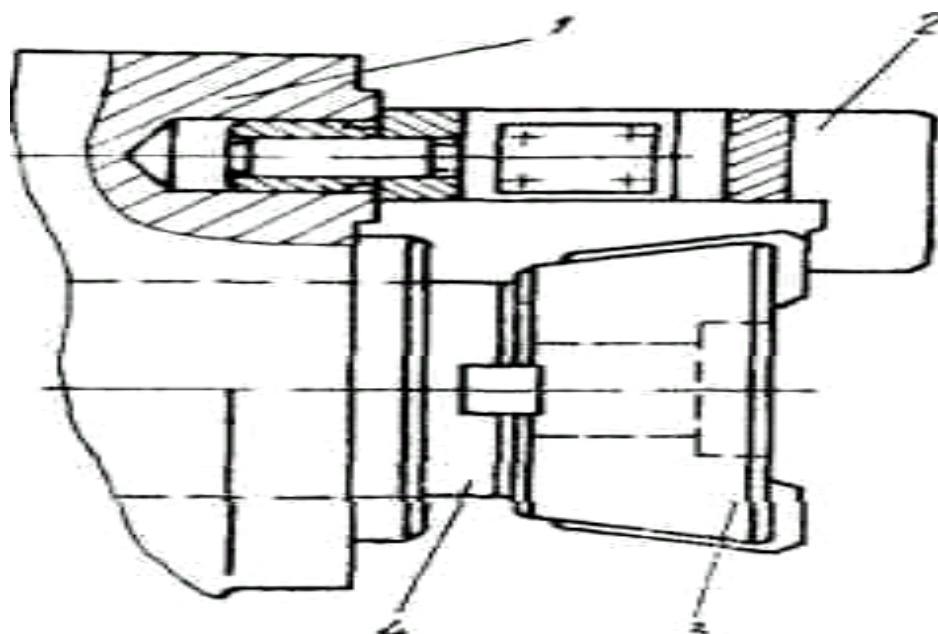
Налагодження торцевої фрези на розмір по шаблону
